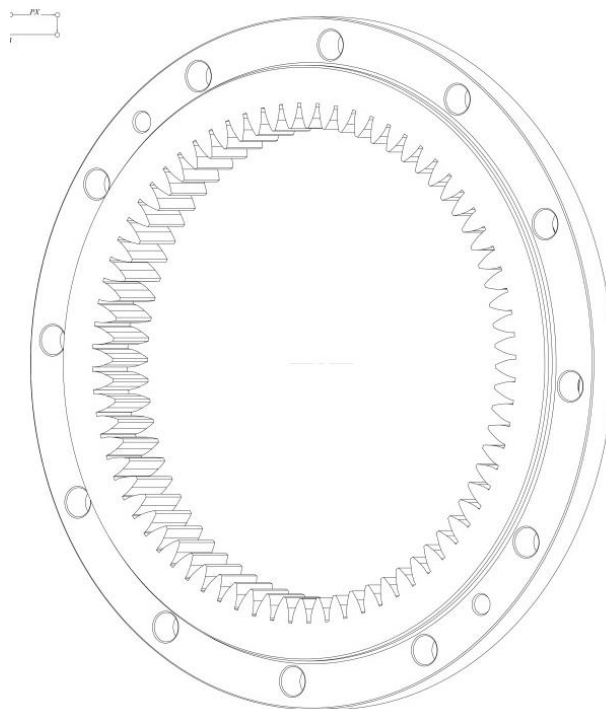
Зовнішній вигляд деталі шестерня «Шестерня МБК34М4568»
